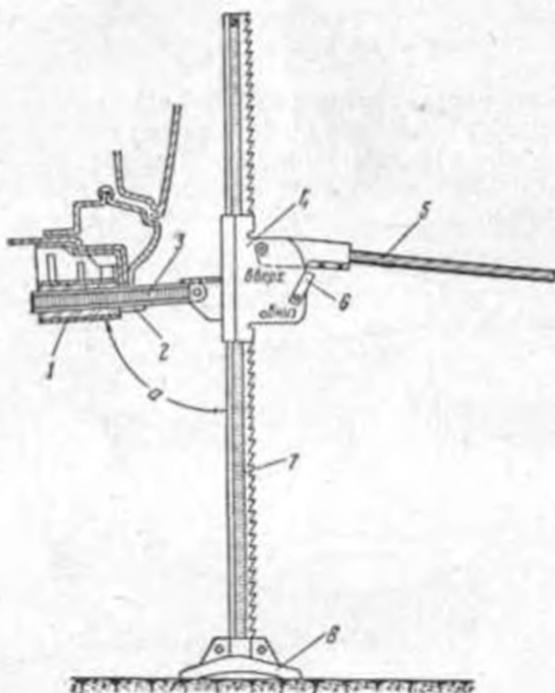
Установка домкрата для вывешивания колеса автомобиля
